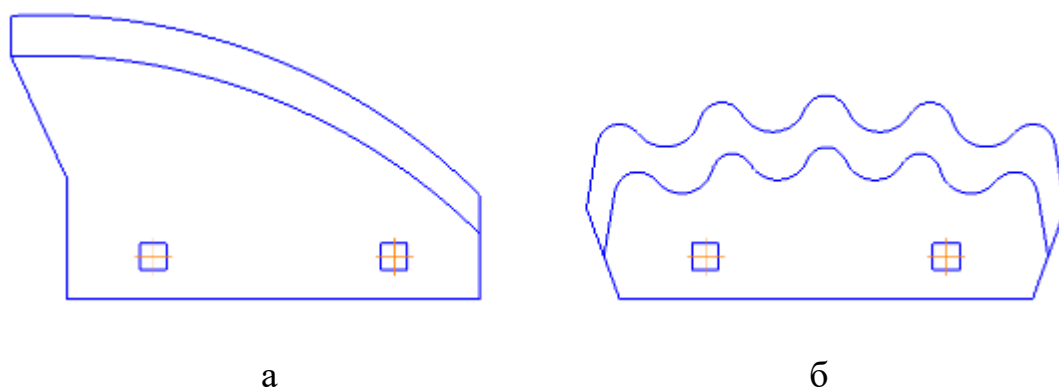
Конструкція ножів змішувально-подрібнювального шнека: а – стандартний; б - проектний
